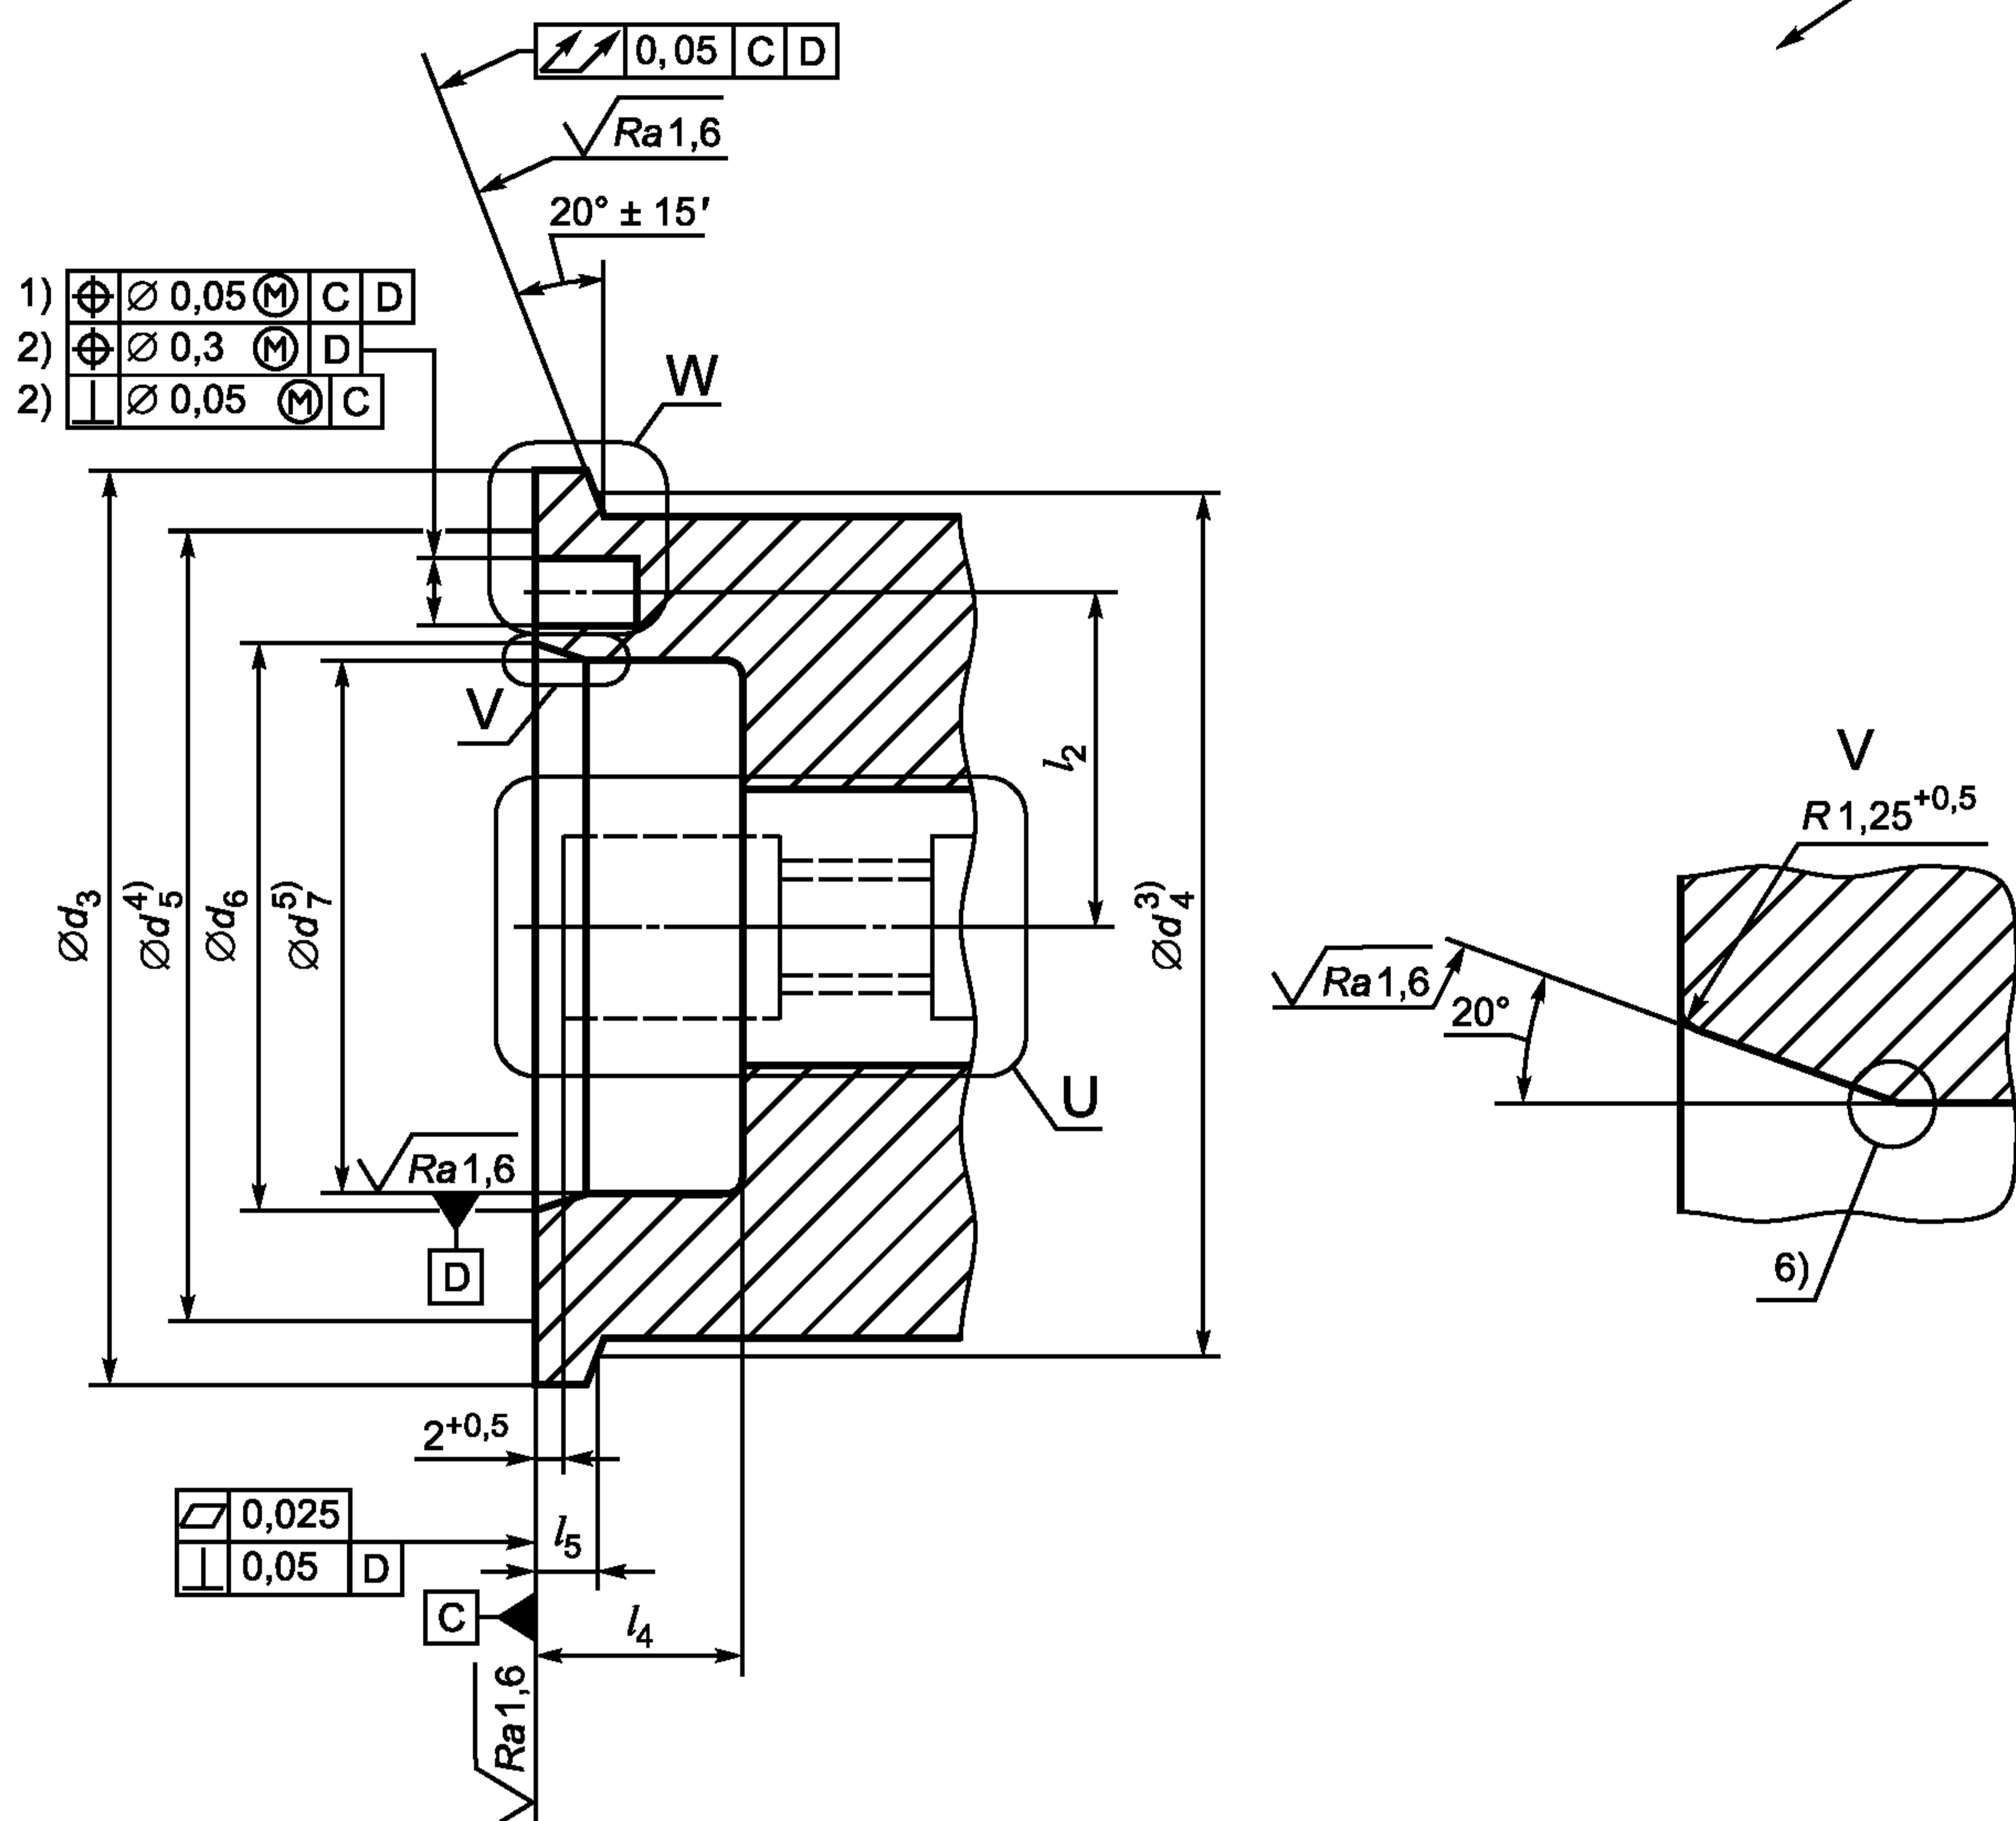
Конструкция и размеры фланцев приводов агрегатов и фланцев двигателя/редуктора (лист 1)
